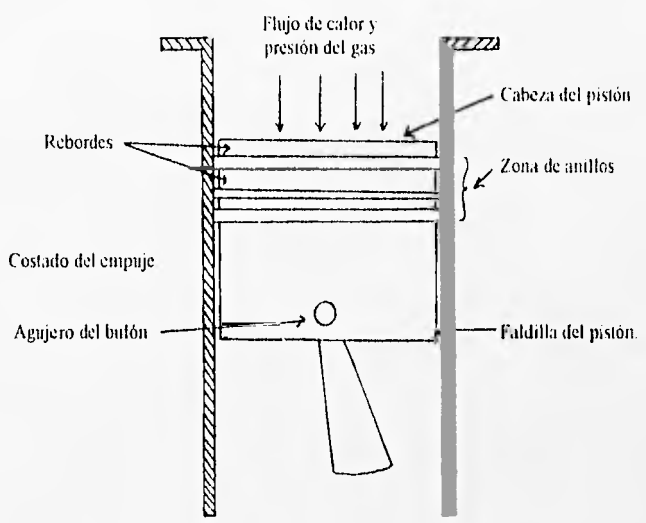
Ensamble de pistón en el interior del cilindro.
